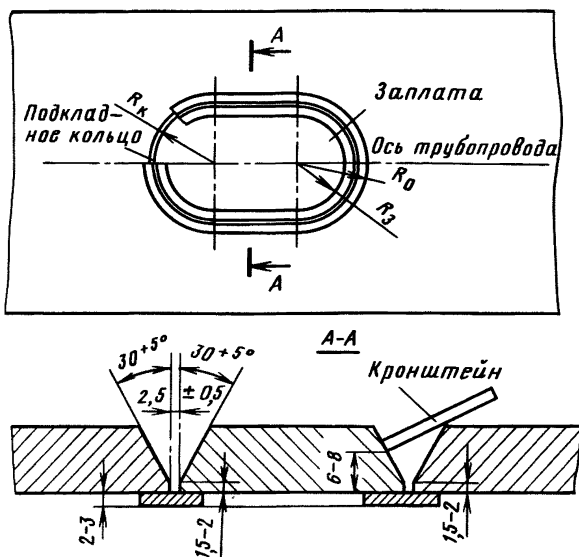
Форма и ориентация отверстия, заплата подкладного кольца и схема разделки кромок под сварку:
